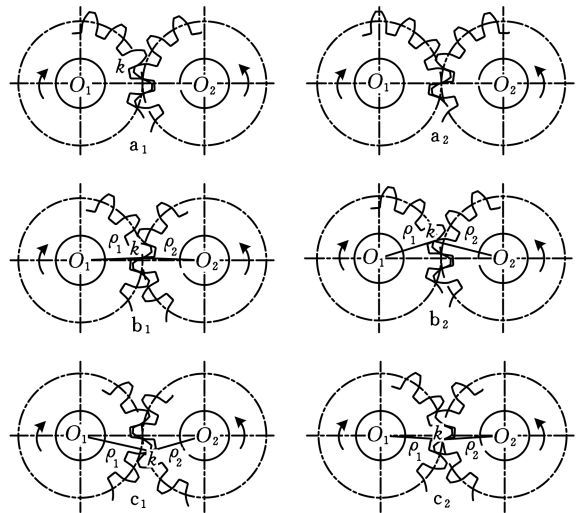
弧齿圆柱齿轮泵的齿轮副啮合状态图
